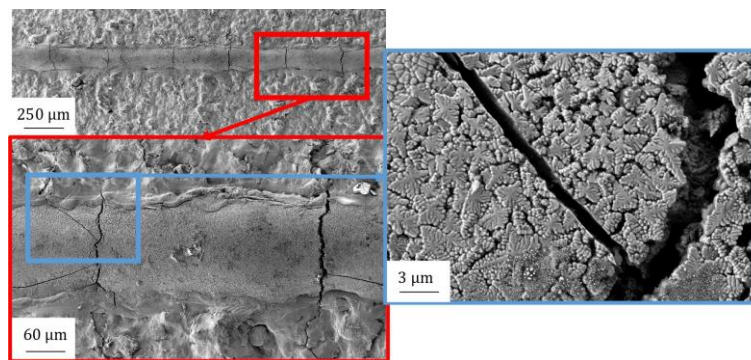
Fissuration en vue de dessus, dépôt MP-A-100, 800 mm/s - 320W - 0,4 J/mm
